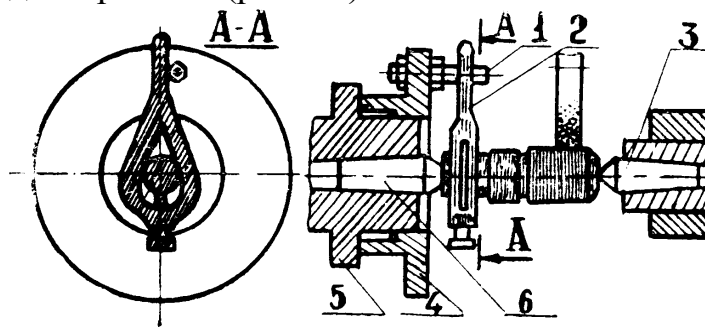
Установка заготовки в центрах круглошліфувального верстата:
